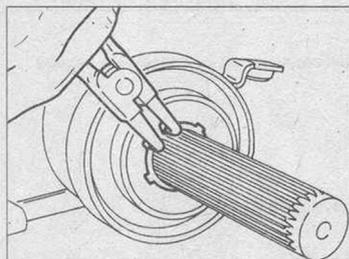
Извлечение стопорного кольца подшипника (Глава 3)
